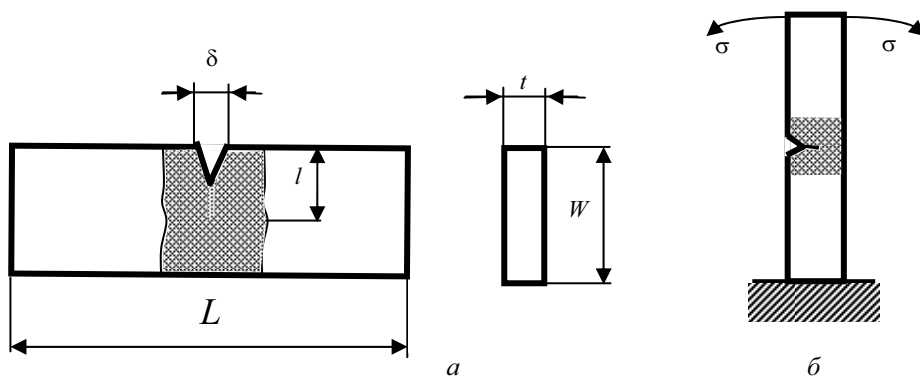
Образцы для усталостных испытаний (а, штриховкой указано расположение зоны сварного шва) и схема нагружения образца (б)
